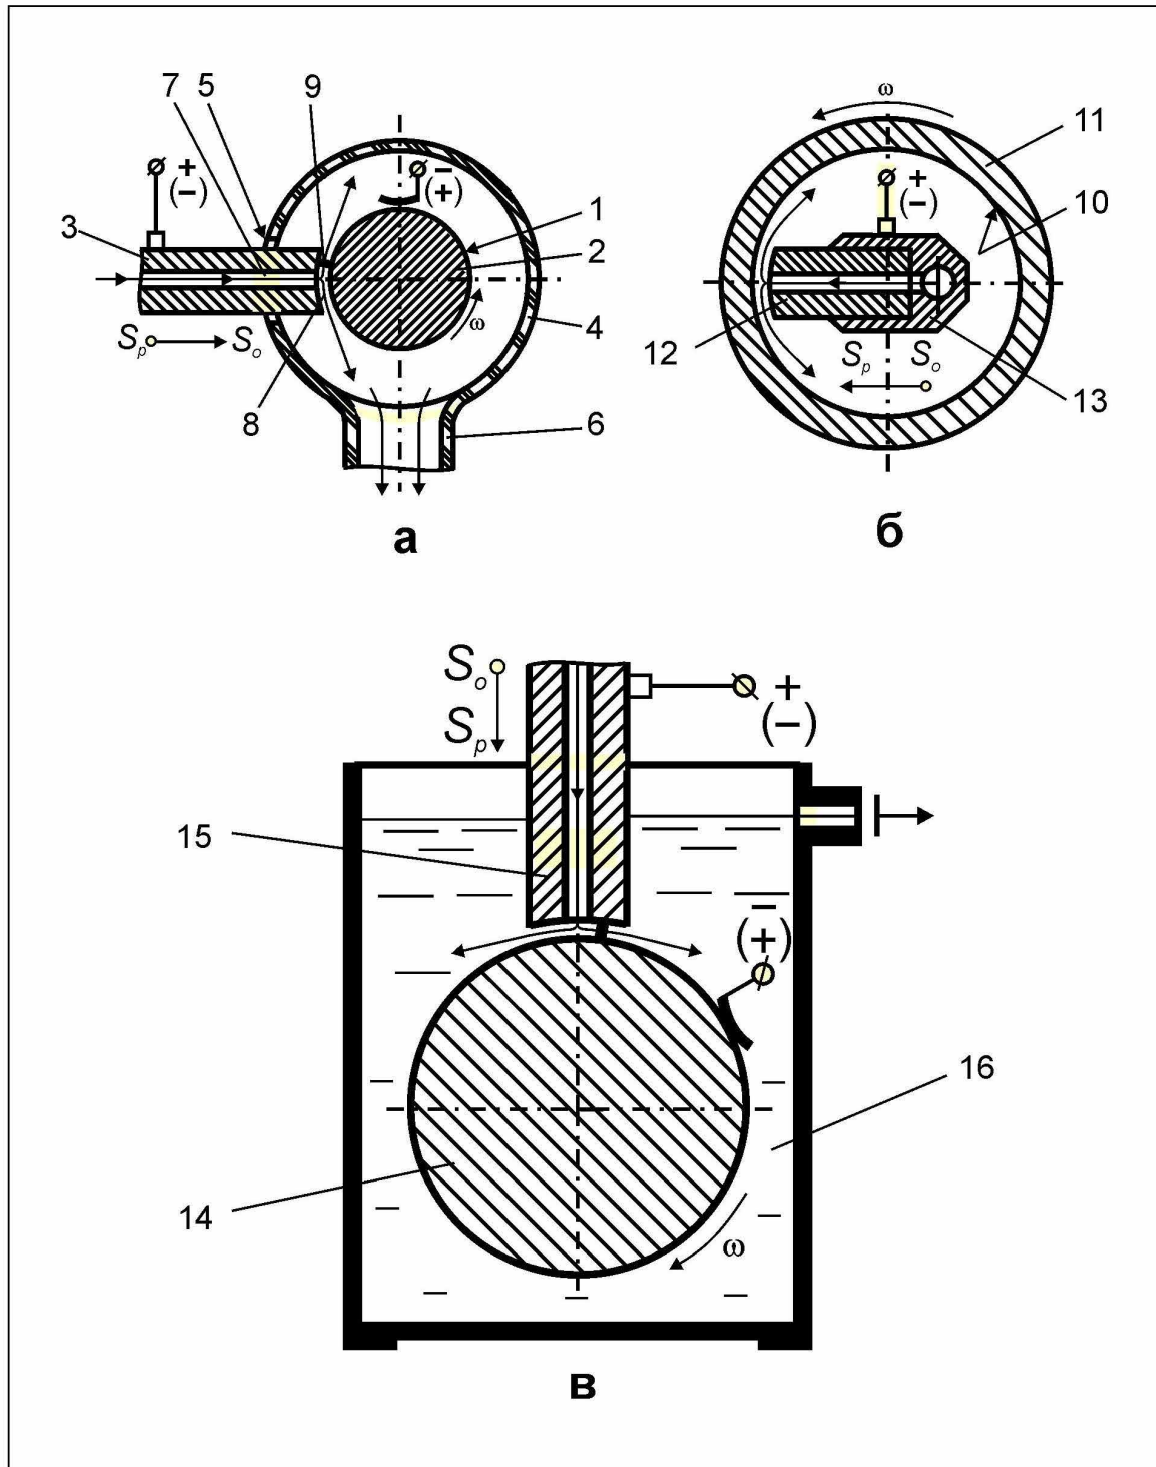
Схема відомого способу РОД тіл обертання графітовим ЕІ, що не обертається: 1 – зовнішня поверхня; 2, 11, 14 – електрод-заготовка; 3, 12, 15 – електрод-інструмент; 4 – прозора камера; 5 – осьовий паз (отвір); 6 – патрубок; 7 – канал; 8 – потік; 9 – дуга; 10 – внутрішня поверхня; 13 – тримач; 16 – робоча рідина
